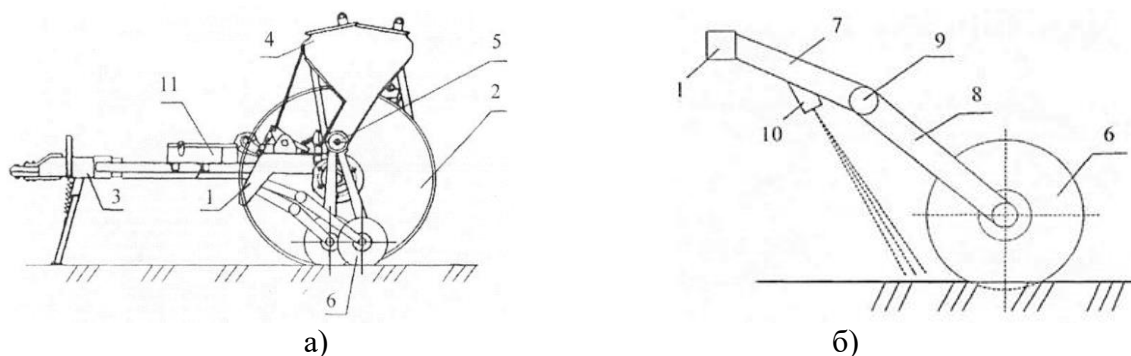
Загальний вигляд зернової сівалки (а) та конструктивна схема механізму кріплення сошника до рами (б)
